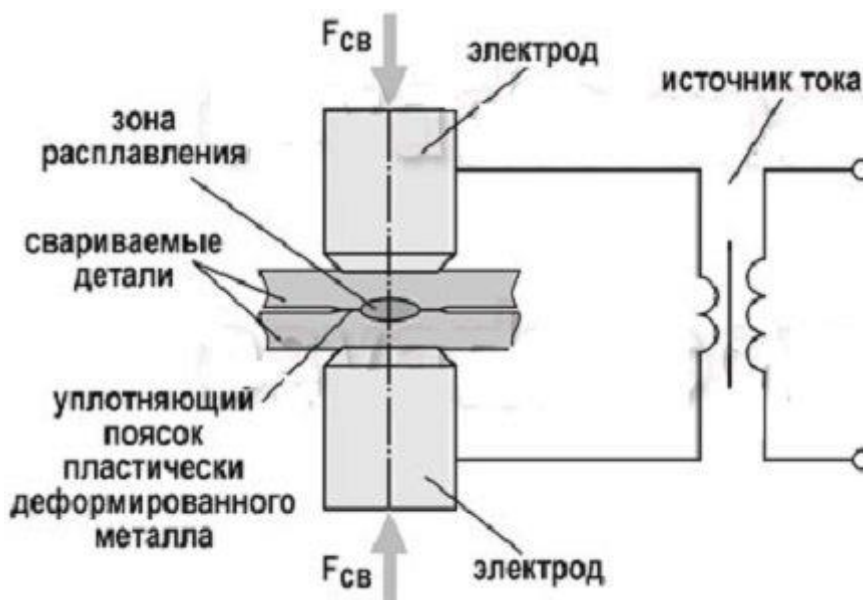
Принцип работы точечной сварки
